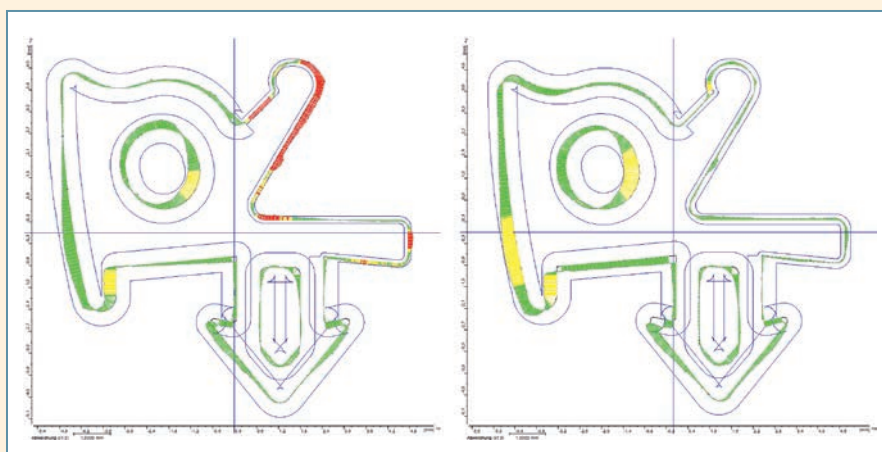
Bei Einpassung der gemessenen Kontur auf die Sollkontur mit BestFit scheint das Werkstück nicht funktionsfähig (links) – die Einpassung mit ToleranceFit berücksichtigt dagegen die Zusammenhänge zwischen den Toleranzen (rechts).
